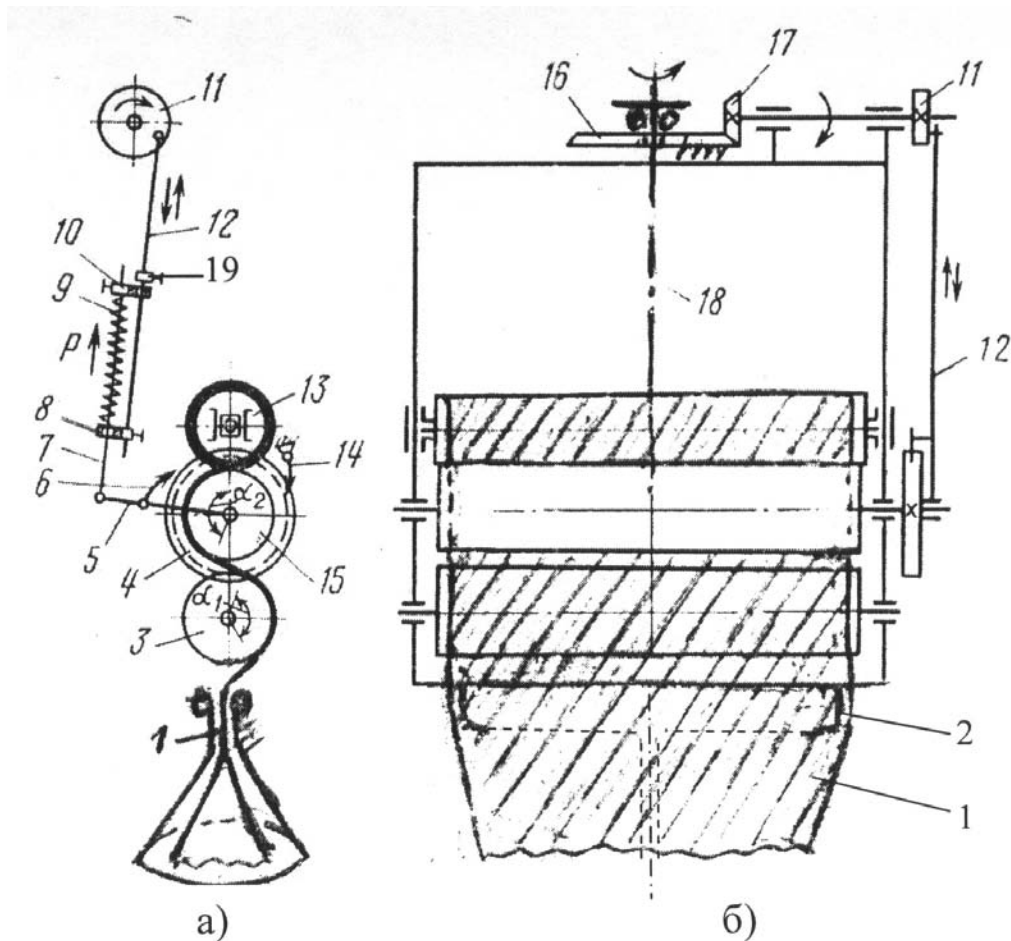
Кинематическая схема валичного обгонного механизма оттяжки машины типа КТ: вид сбоку (а), вид спереди (б);
